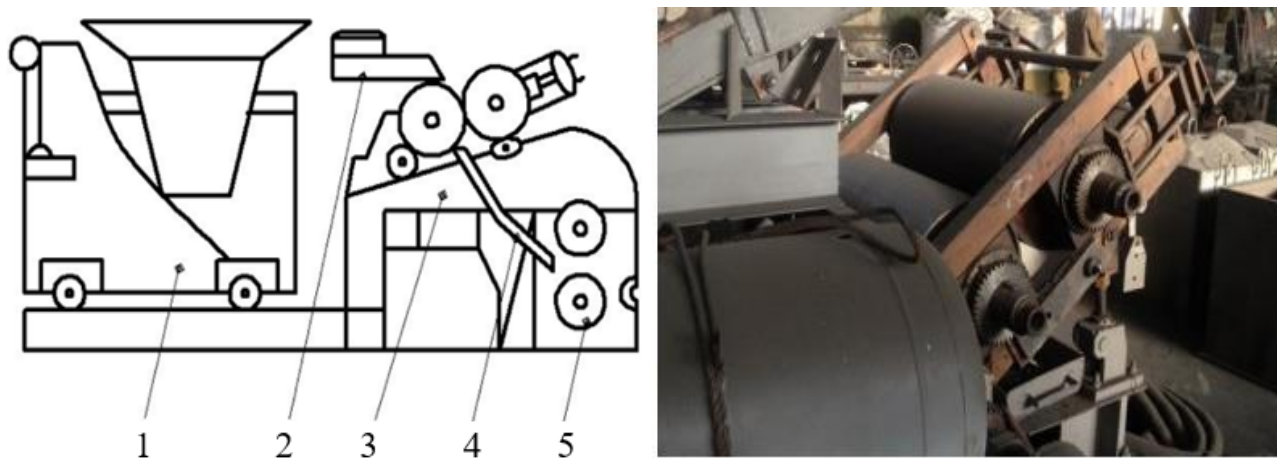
Лабораторна установка для валкової розливки металевих сплавів:
